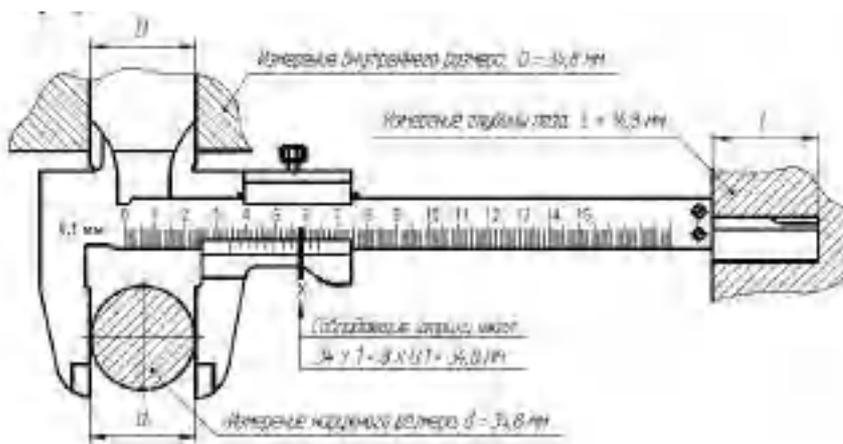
Измерение размеров деталей штангенциркулем типа
